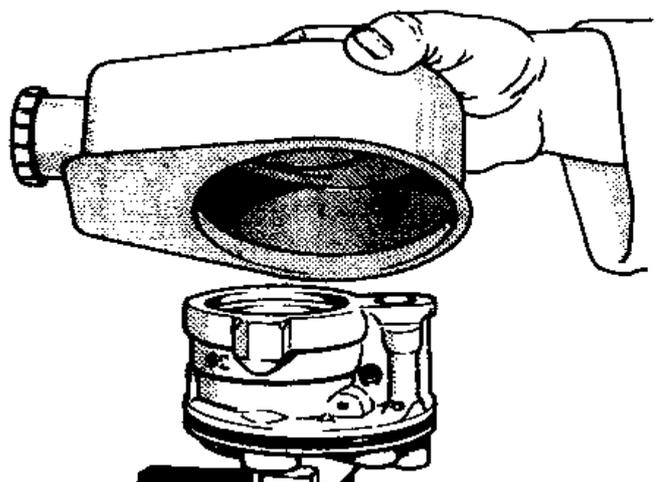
Снятие резервуара с корпуса (Разд.41)
